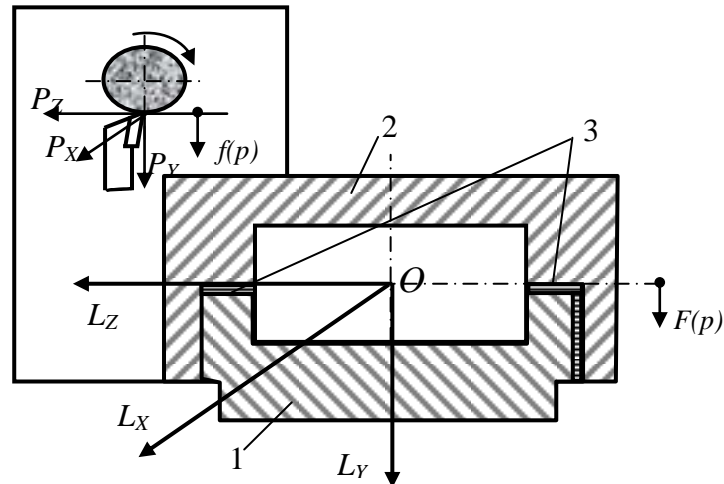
Схема стику «направляючі каретки – горизонтальні направляючі станини»: 1 – станина верстату; 2 – каретка револьверного супорту; 3 – стик
